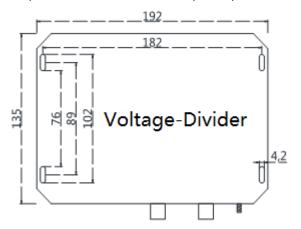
Размеры делителя напряжения контроллеров ТНС F1627S/F1627D/F1628S/F1628D.
